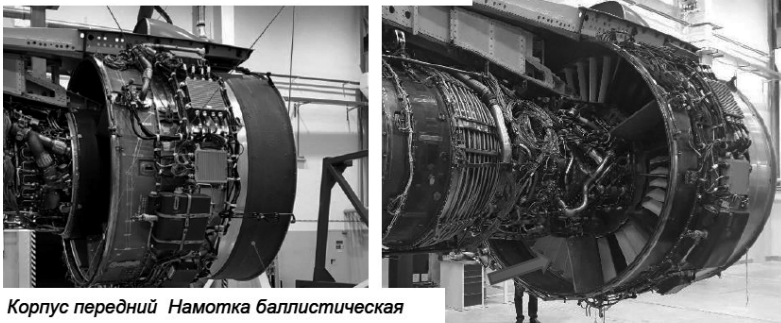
Корпус вентилятора и вид на СА вентилятора
